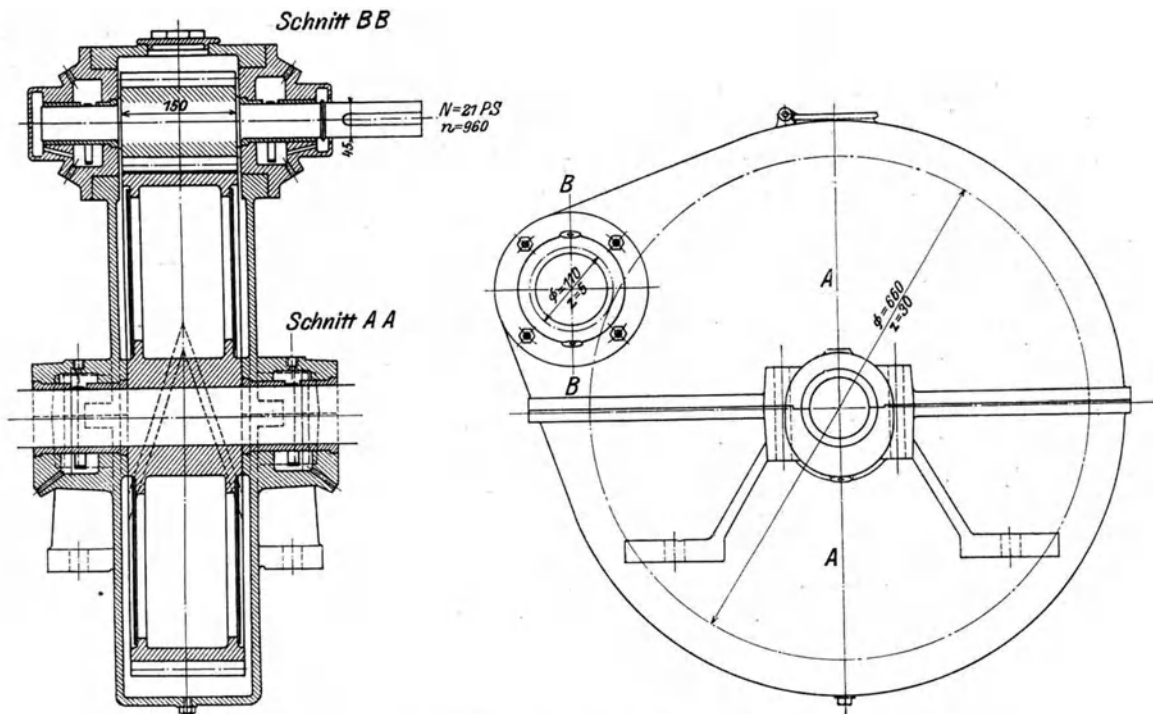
Ausführung der Zahnradfabrik Augsburg, vorm. J. Renk.
